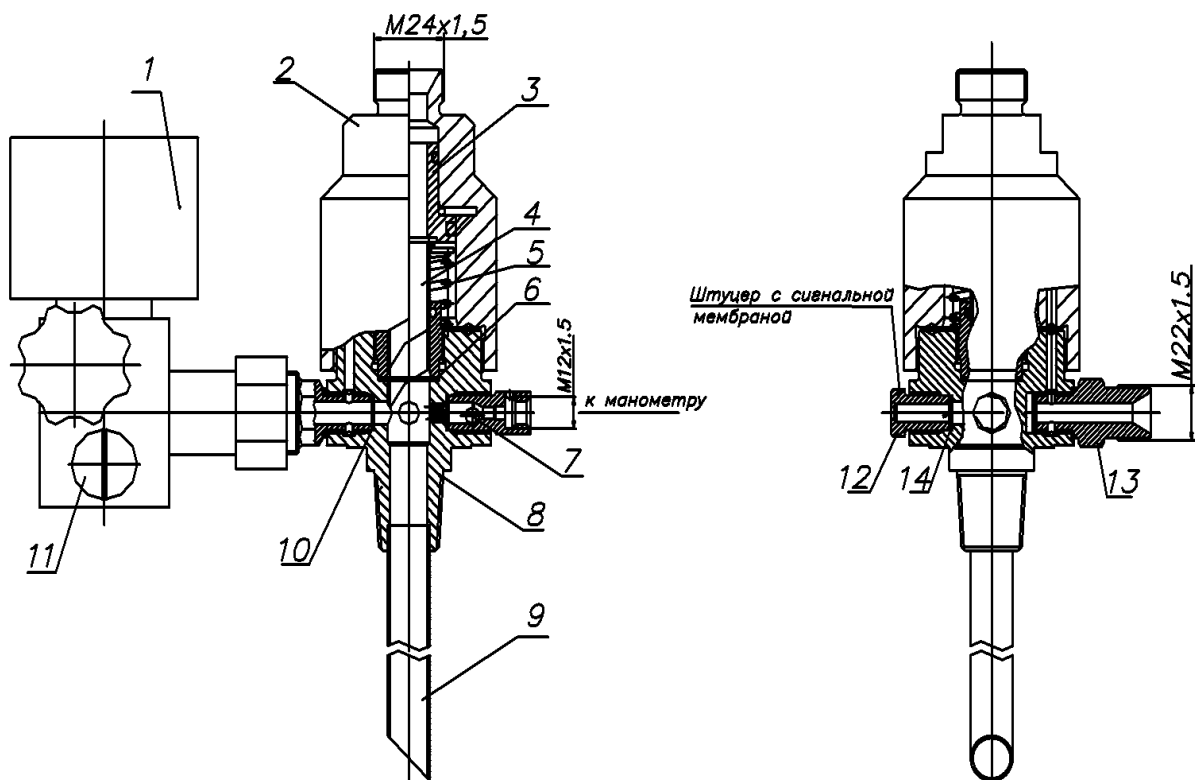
Запірно-пусковий пристрій: 1 - ППЕ; 2 - ковпак; 3 - поршень; 4 - фреза; 5 - пружина; 6 - мембрана робоча; 7 - кулька; 8 - корпус; 9 - трубка сифона; 10 - мембрана; 11- кнопка ручного пуску; 12 - штуцер; 13 - штуцер; 14 - мембрана запобіжна
